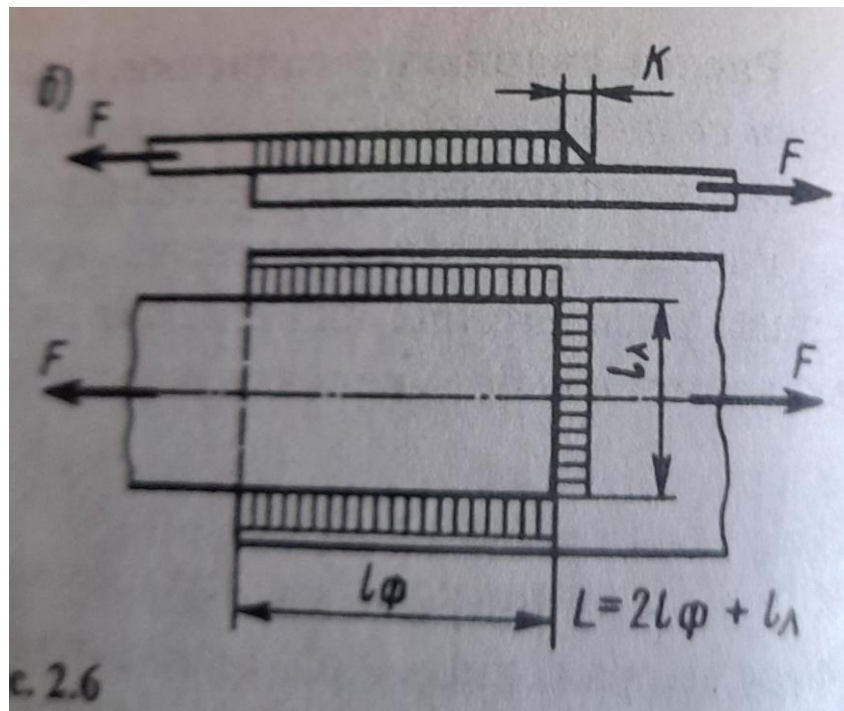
Нахлесточный сварной шов
